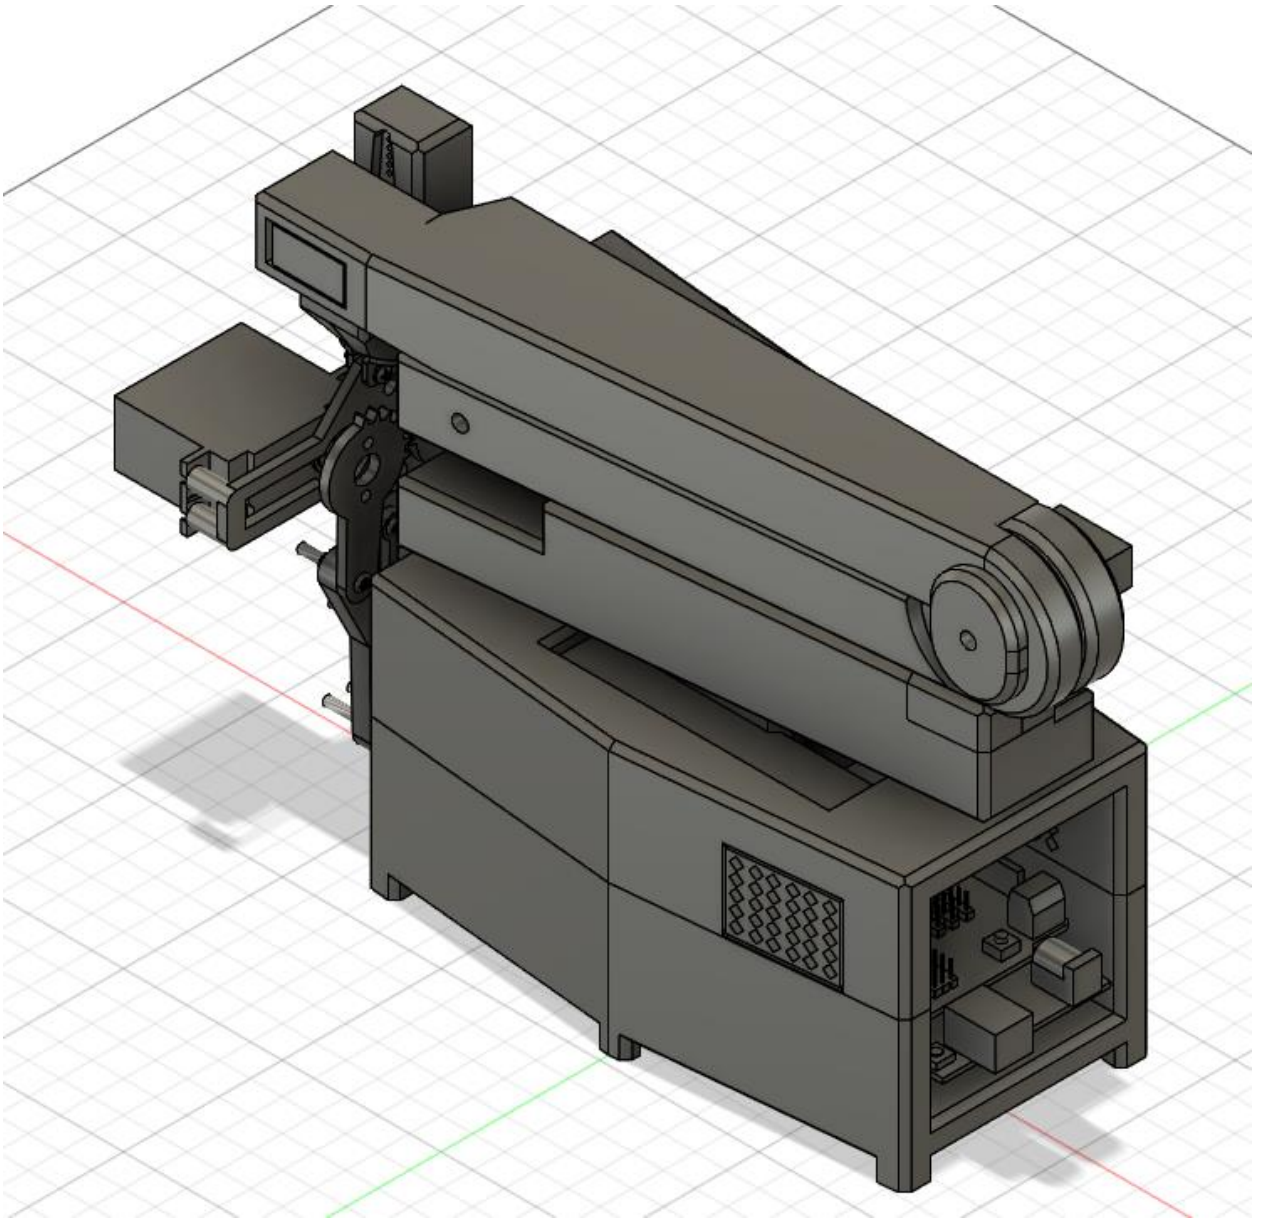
Ізометричний вид на корпус маніпулятора в стані «сну» (Вид 2)
